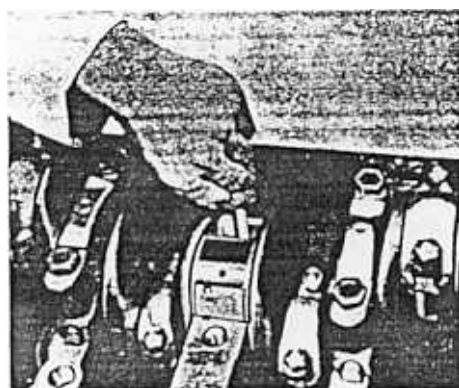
A 13A 01 .. Desmontaje de un cojinete superior de bancada
